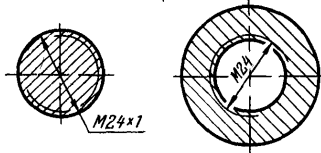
Обозначение метрической резьбы наружным диаметром 24 мм с мелким шагом 1 мм и крупным шагом
